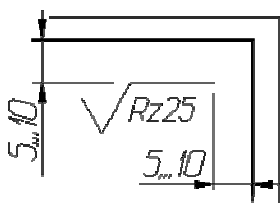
Указание шероховатости одинаковой для всех поверхностей изделия
